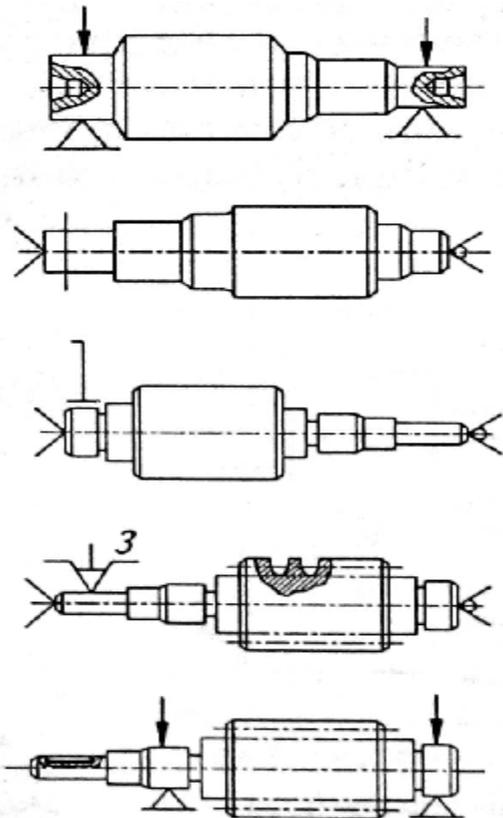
Черновое и чистовое базирование при изготовлении вала из поковки
